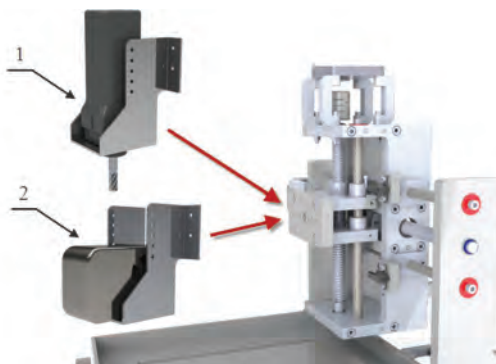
Сменные модули станка портального типа с ЧПУ
